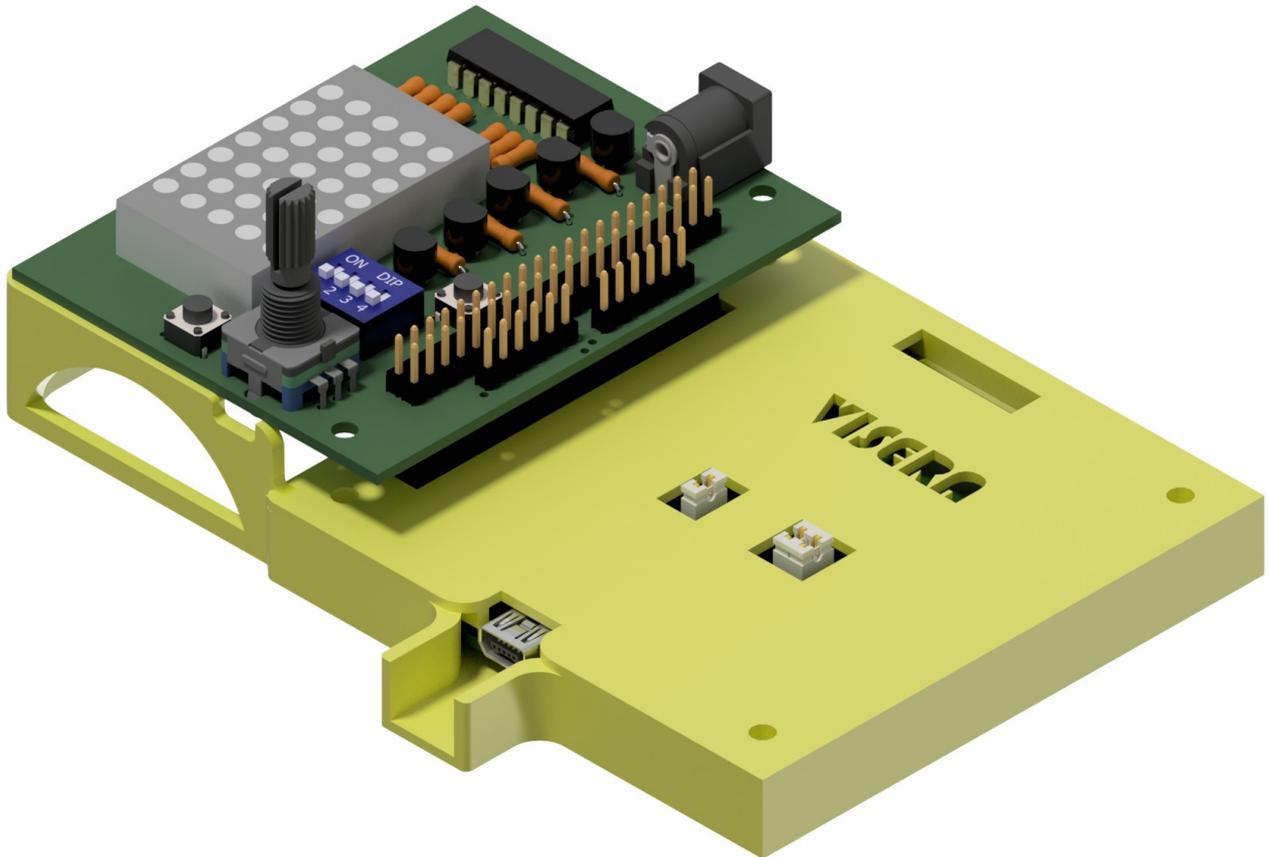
Modelo de gabinete propuesto para contener la Visera montada en la Breakout Board
